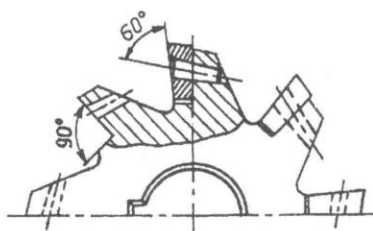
Крепление режущих пластин коническими штифтами в пазах корпуса фрезы
